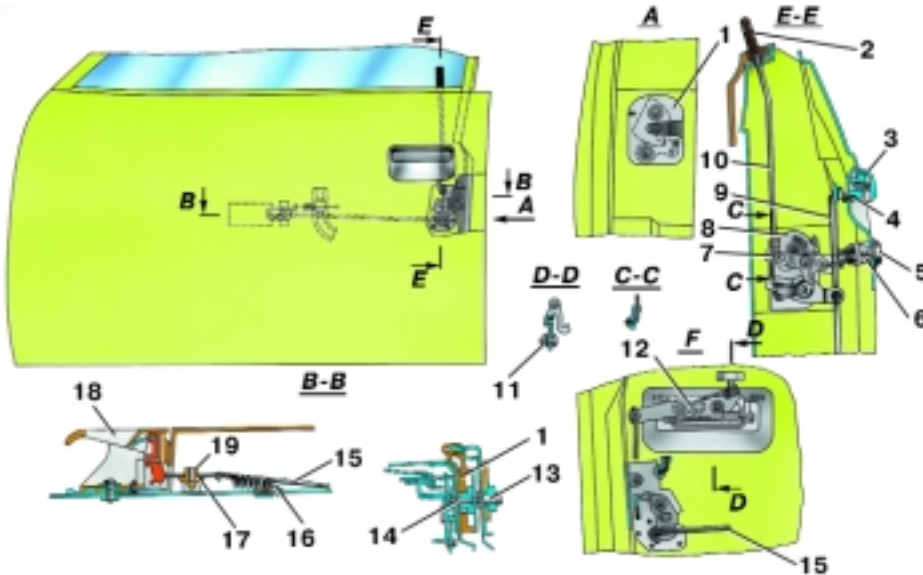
Установка замков и ручек передней двери: 1 – наружный замок; 2 – кнопка блокировки замков; 3 – наружная ручка; 4 – болт крепления наружной ручки; 5 – выключатель замка; 6 – держатель выключателя; 7 – держатель тяги; 8 – внутренний замок; 9 – тяга наружного привода; 10 – тяга кнопки блокировки; 11 – гайка; 12 – рычаг наружного привода; 13 – защелка; 14 – винт крепления замков; 15 – тяга внутреннего привода; 16 – пружина тяги внутреннего привода; 17 – опора тяги внутреннего привода; 18 – ручка внутреннего привода; 19 – втулка опоры тяги
